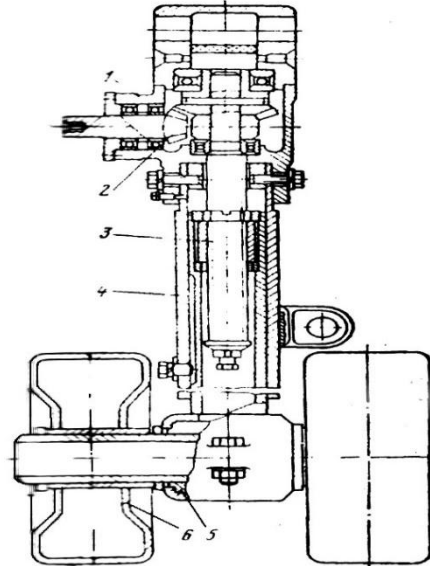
Опорний пристрій напівпричепа МАЗ-5215Б:
